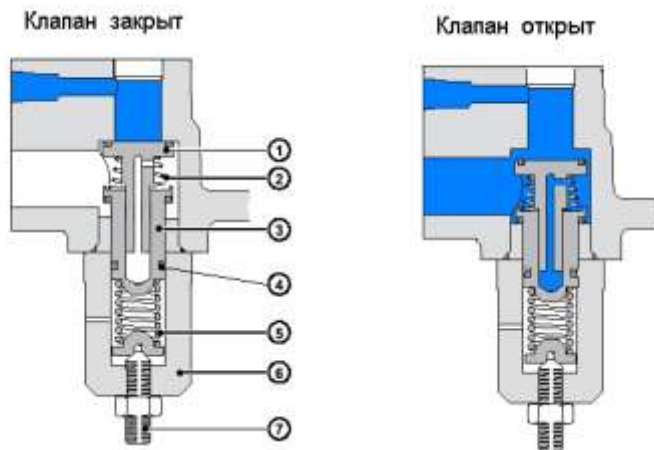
Схема клапана минимального давления: 1 – тарелка обратного клапана; 2 – пружина обратного клапана; 3 – поршень; 4 – кольцо уплотнительное; 5 – пружина клапана минимального давления; 6 - корпус; 7 – винт регулировочный.
